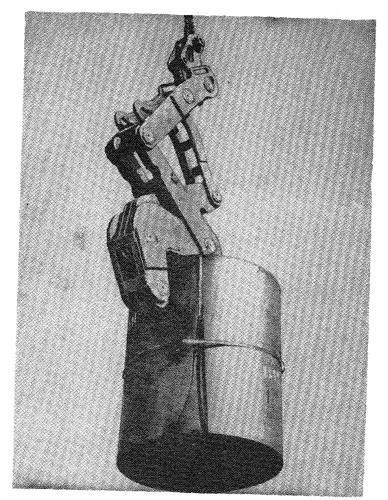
Рис. IIII.I.Крановий автоматический захват для перегрузки стального листа в рулонах конструкции ЧЦКБ
